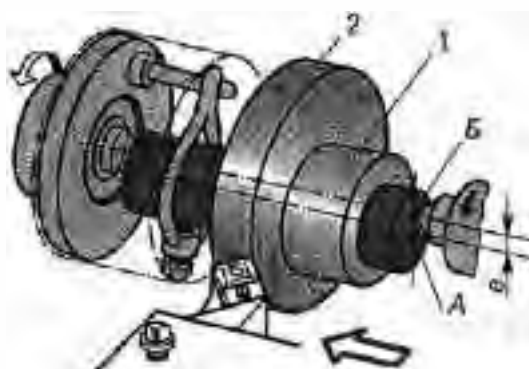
ОБРОБКА ЕКСЦЕНТРИЧНОГО ДИСКА НА ЦЕНТРОВІЙ ОПРАВЦІ
